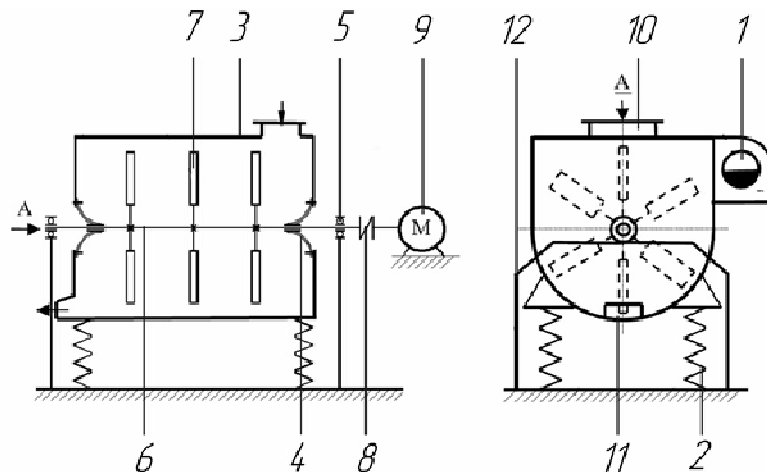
Схема вібраційного змішувача: 1 – рама; 2 – пружина; 3 – корпус змішувача; 4 – поліуретанове ущільнення; 5 – підшипникові опори; 6 – вал; 7 – лопатки; 8 – втулково-фланцева муфта; 9 – редуктор; 10 – муфта; 11 – електродвигун; 12 – віброзбуджувач
